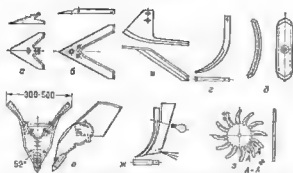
Рабочие органы культиватора: а — универсальный двухсторонний лапа; б — стрельчатая двухсторонняя лапа; в — стрельчатая односторонняя лапа; г — доломобразная расклевывающая лапа; д — ошкунчик; е — шарообразный нож; ж — покатый диск.
